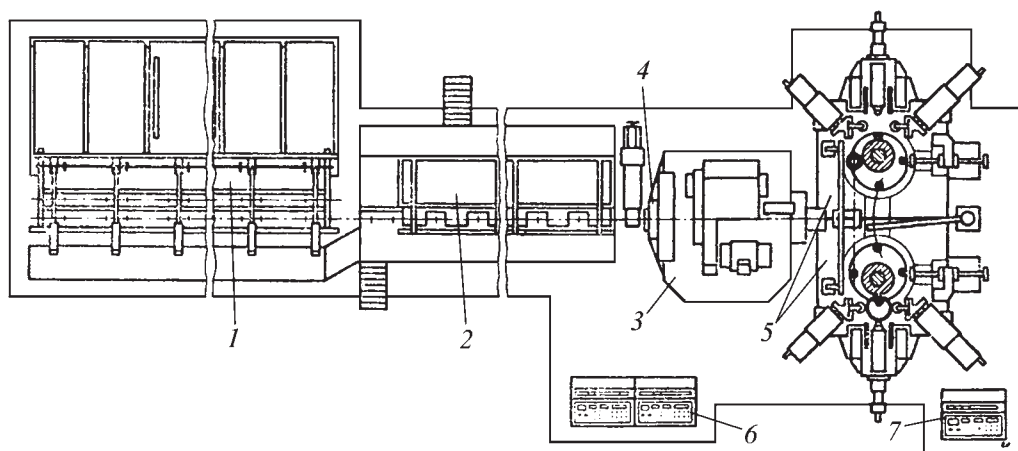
Компоновка автоматической линии для крупносерийного производства кольцевых заготовок:
